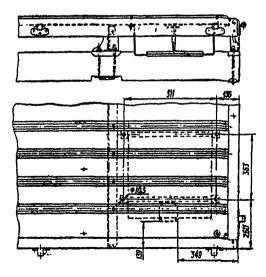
Установка инструментального ящика на автомобили ГАЗ-53-07 и ГАЗ-52-08
